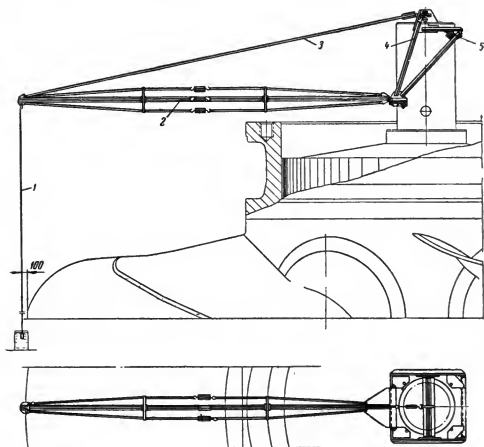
Схема проверки концентричности лопастей рабочего колеса.
